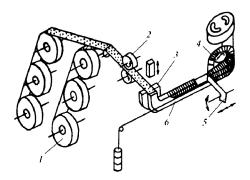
Схема установки механизированной сборки лепестковых кругов:
